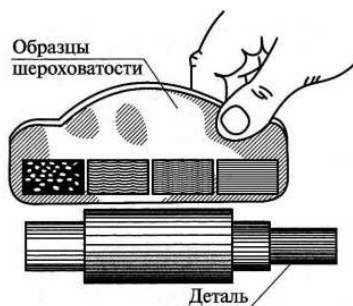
Метод сравнения с образцами, прибор для определения параметров шероховатости
